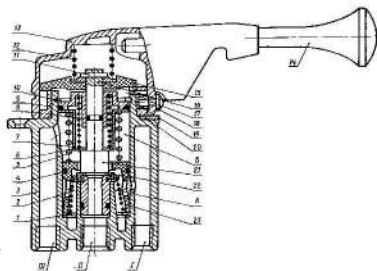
Тормозной кран обратного действия с ручным управлением: 1—упорное кольцо; 2—пружина клапана; 3—корпус; 4—уплотнительное кольцо; 5—уравновешивающая пружина; 6—пружина штока; 7—тарелка пружины; 8—направляющая штока; 9—обойма; 10—упорное кольцо; 11—штифт; 12—пружина; 13—крышка; 14—рукоятка; 15—направляющий колпачок; 16—шток; 17—ось ролика; 18—фиксатор; 19—ролик; 20—стопор; 21—выпускное седло клапана на штоке; 22—клапан; 23—следящий поршень; I—вывод к воздушному баллону; II—атмосферный вывод; III—вывод управляющей магистрали
